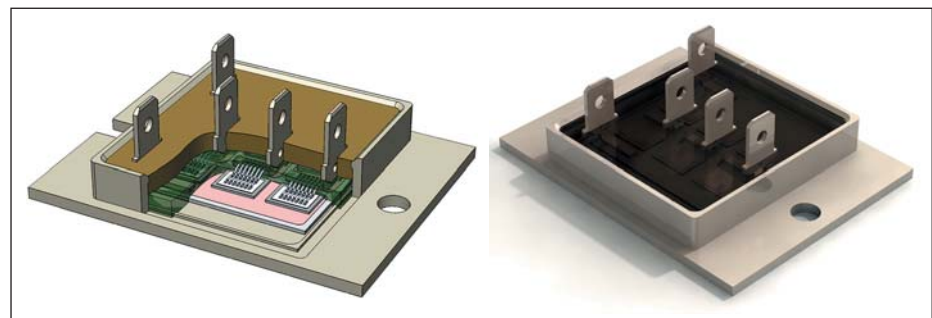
Конструкция и внешний вид корпуса для 30-амперных мостов
